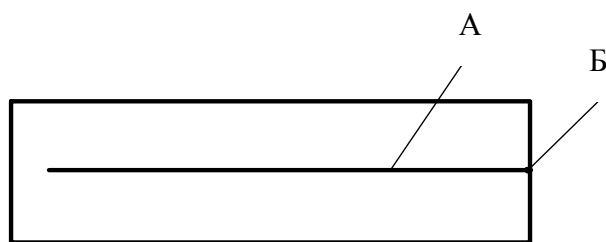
Образец для сварки (А – рез; Б – прижим)
